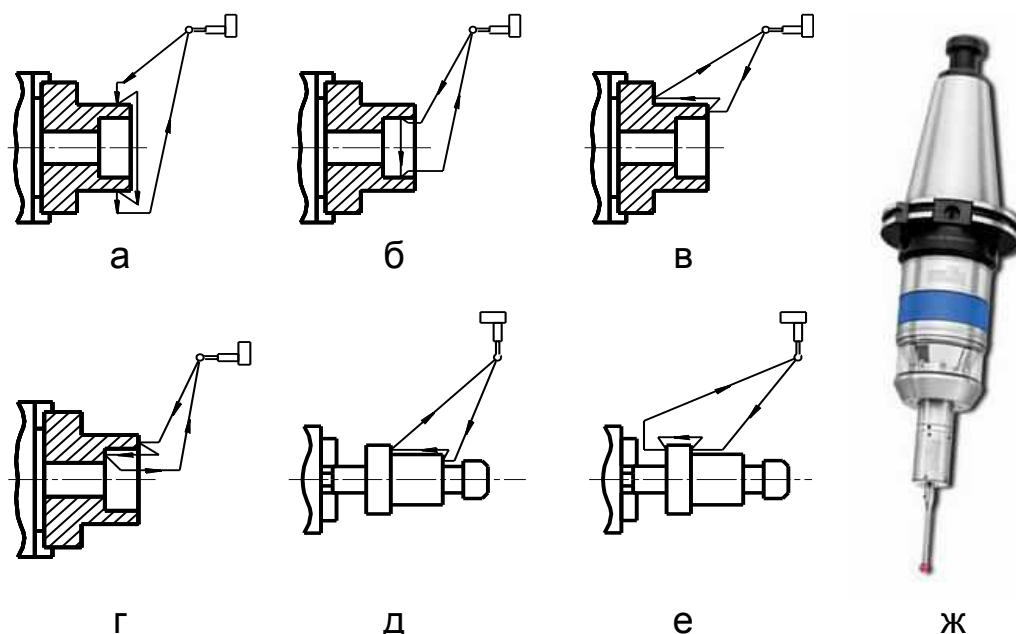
Типові схеми застосування ВГ для вимірювання: а, б – залежно від зовнішнього й внутрішнього діаметрів; в, г, д – довжини обробленої поверхні; е – товщини фланця; ж – загальний вигляд щупа в інструментальній оправці
